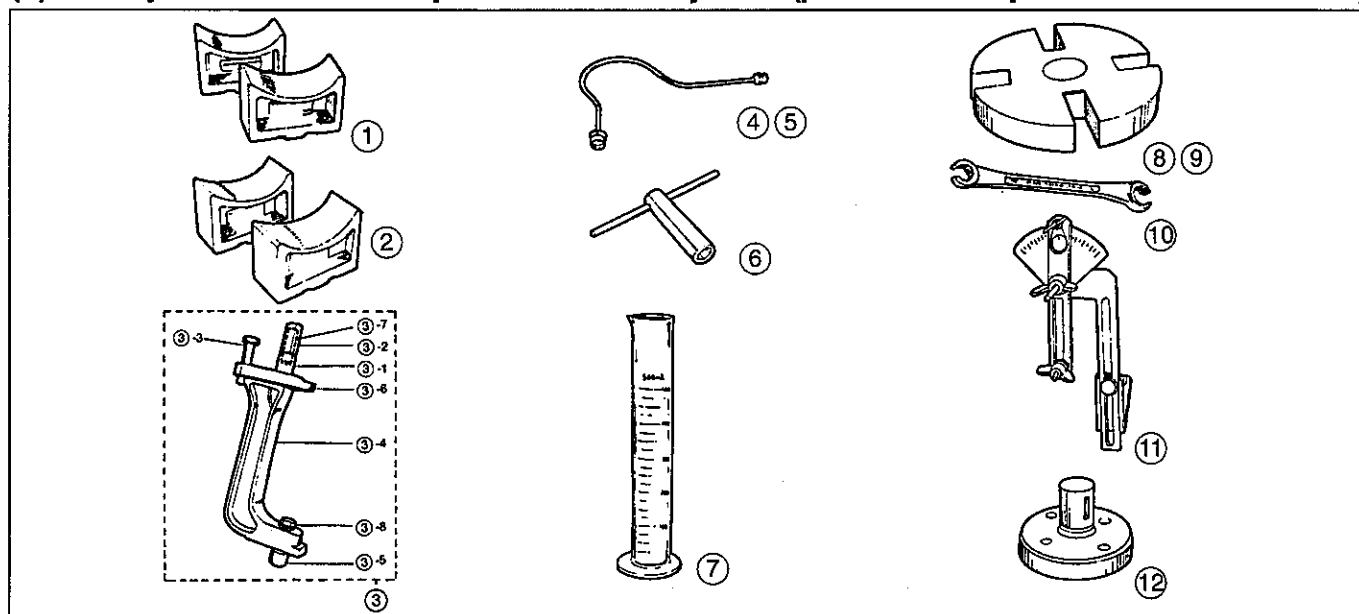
Conjunto de accesorios para bomba PE-A y PE-B
